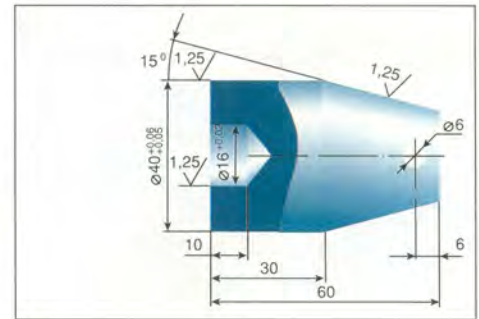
Оправка для установки крышки привода распределительного вала с сальником двигателя ВАЗ–2105 (центрирование по валу привода вспомогательных агрегатов).
